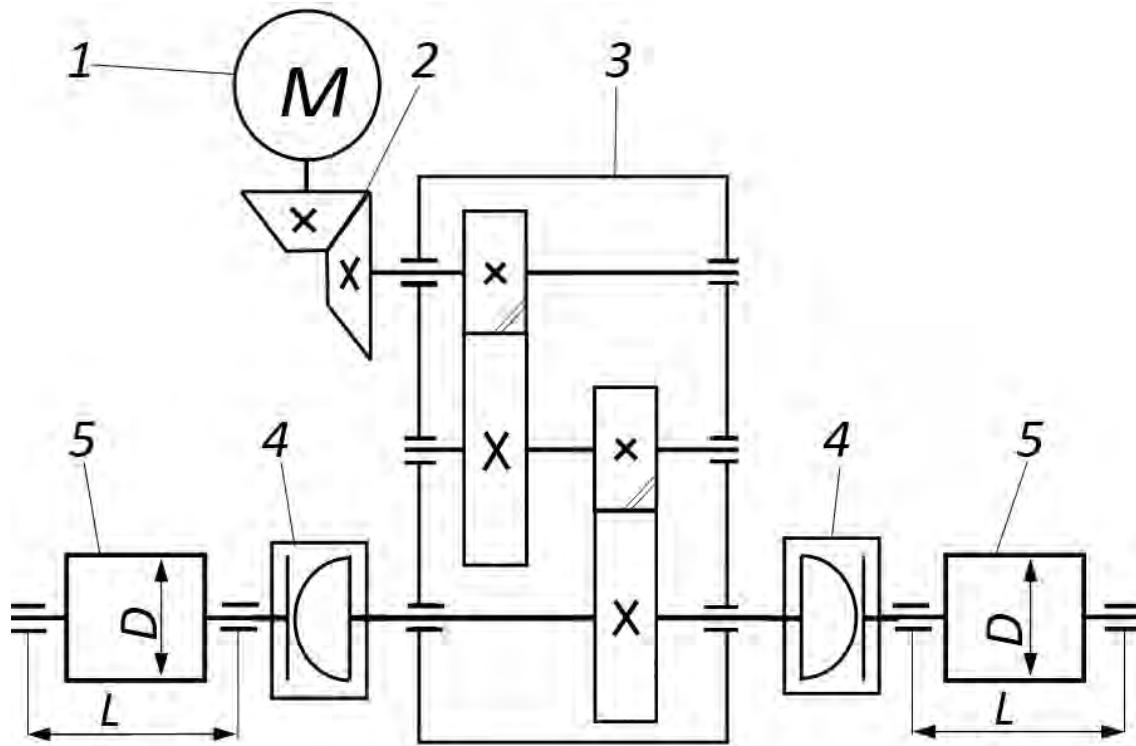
Схема привода ленточного двухпоточного конвейера (вид сверху):
